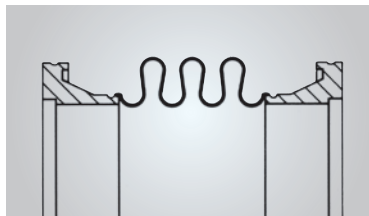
Axial-Kompensator mit Klammerflanschen
